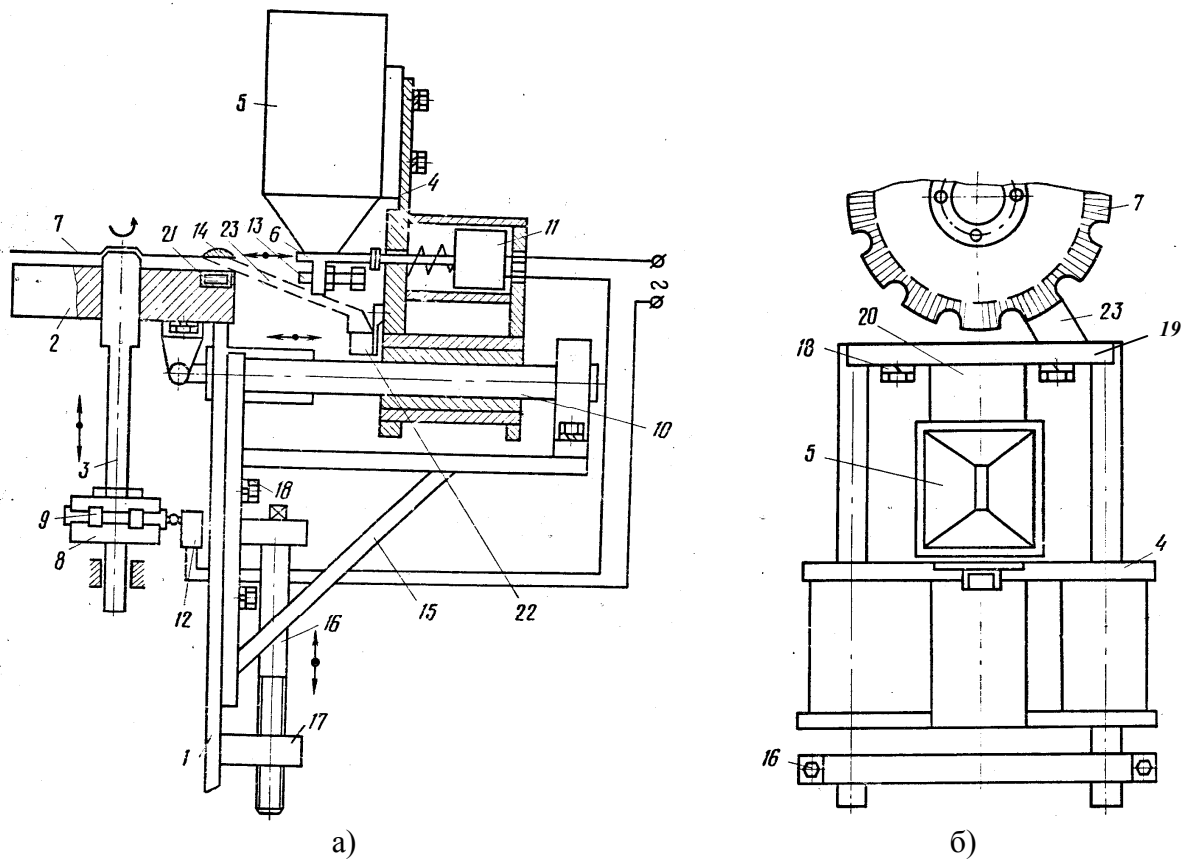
Пристрій для індукційного наплавлення тонких дисків з неперервно-послідовним засипанням порошкоподібного твердого сплаву: а - загальний вид; б - вид зверху
